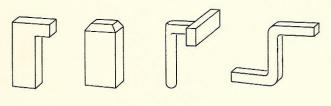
geformte Hand-Vorhaltewerkzeuge
